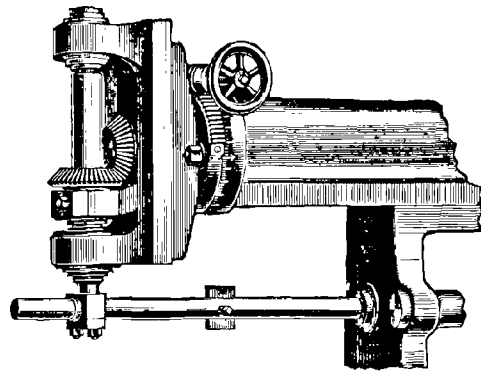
Disposition pour fraiser et aléser horizontalement.
